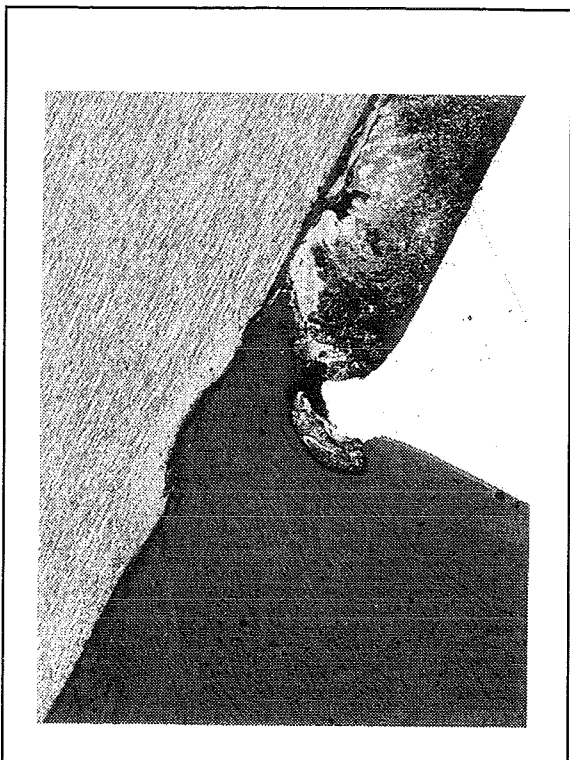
vervuiling van de contactbuis, Meldra 1,6 tweede poging, 100 X vergroot.
